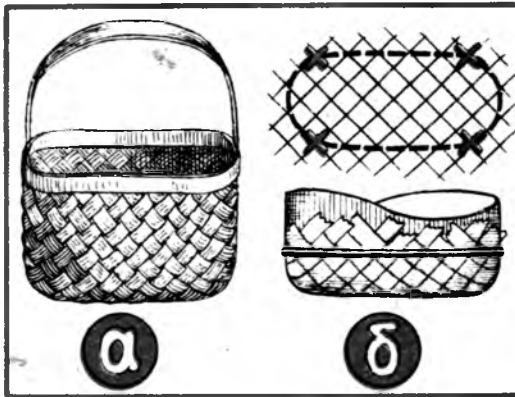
Получение овальной корзины из коробчатого полотна: а — корзина; б — полотно с разметкой мест поворота лент и контурами дна болванки и плетение полотна на болванке под резинкой
